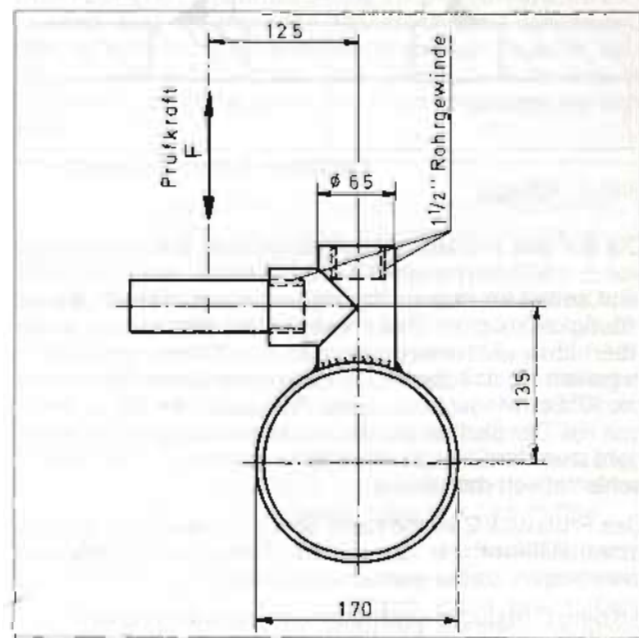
Angeschweißter Hausanschlußstutzen 1 1/2 Zoll
